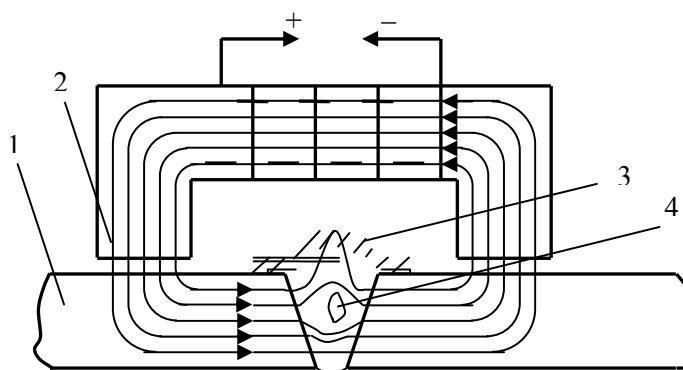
Схема проведения магнитографического контроля сварного шва.
